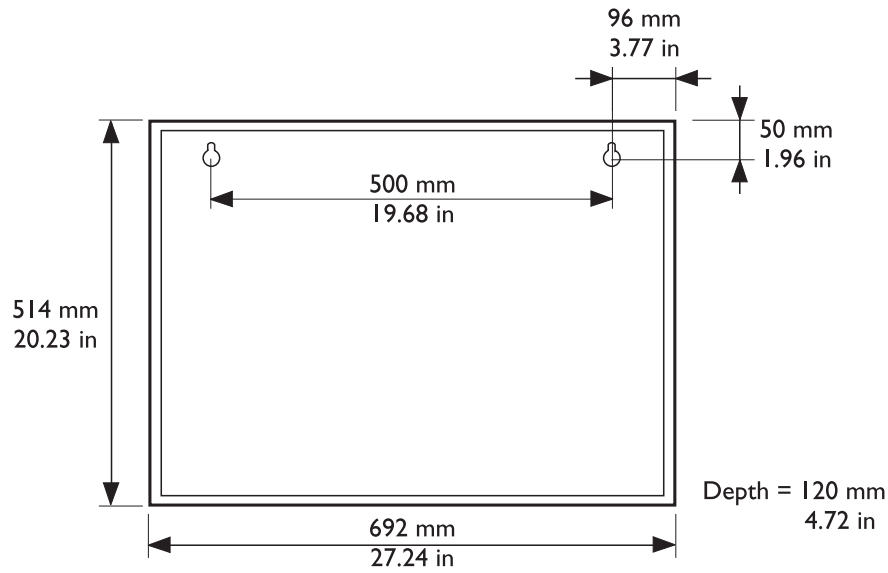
Dimensões de montagem do gabinete de carregamento
